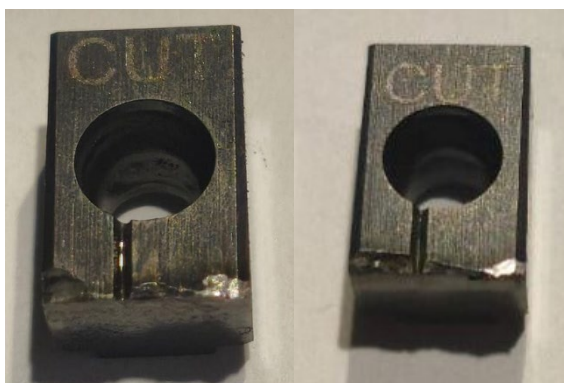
Фотографии износа твёрдосплавных пластин при резке заготовок с подачей на зуб 0,06мм.
